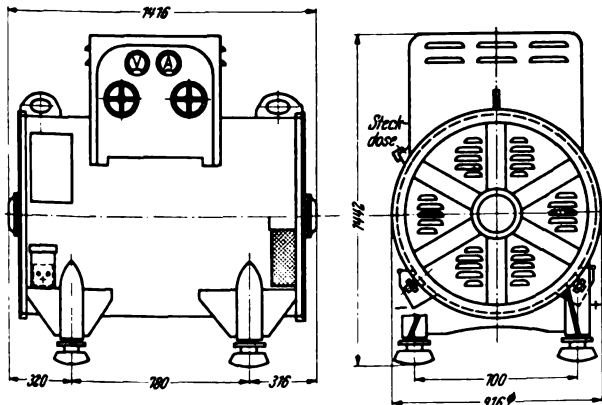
Eingehäusiger Mehrstellen-Schweißumformer.
